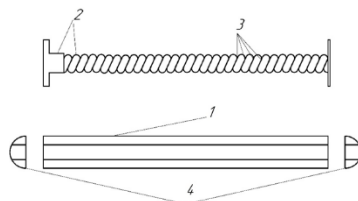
Схема конструкции нагревающейся рабочей секции
